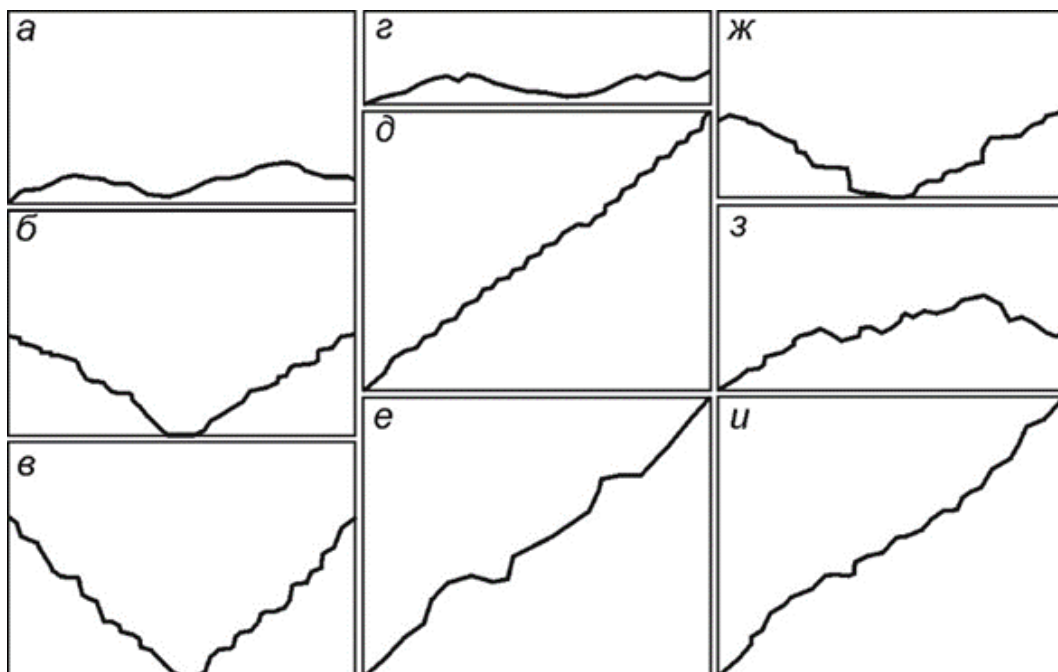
Виды рельефов поверхностей разрушения сварных швов в поперечном разрезе.
